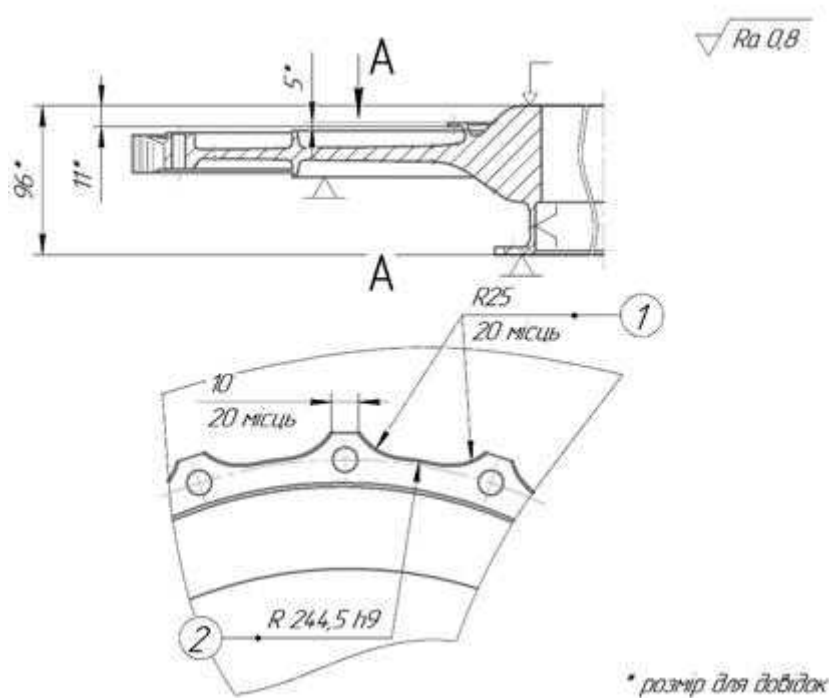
Операційний ескіз на фрезерну операцію
